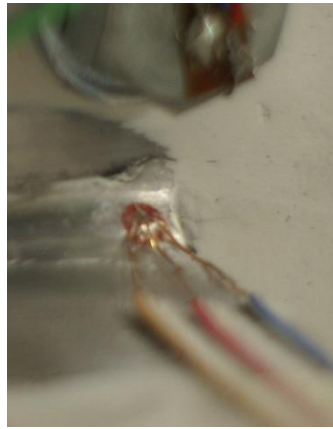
Roseta colocada no cordão de soldadura.
